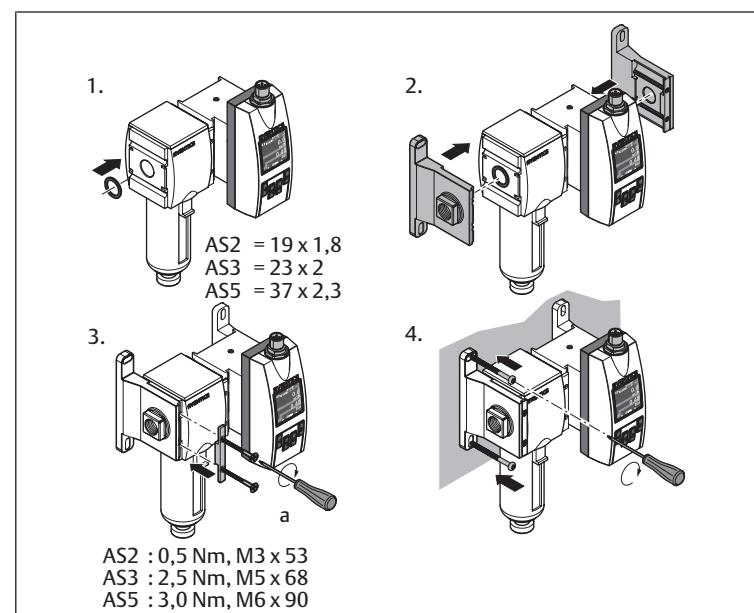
Montaggio con set per il montaggio in batteria | W05
